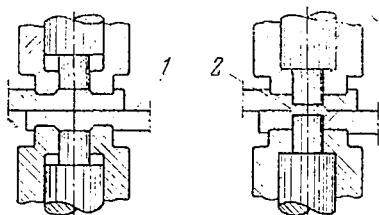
Схема холодной сварки в двух зонах.
